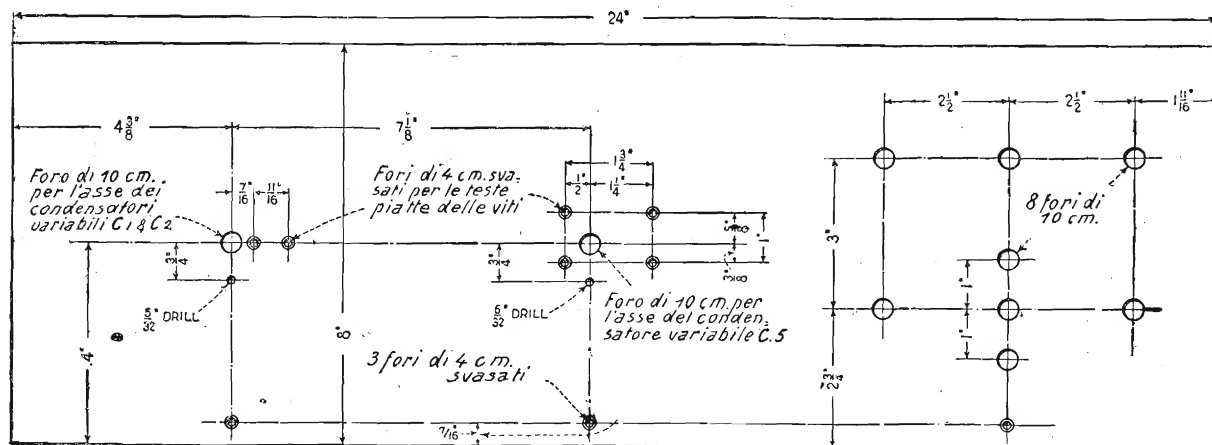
Piano di foratura del pannello frontale. Si noti che usando una basetta di legno le dimensioni delle viti cambiano.
